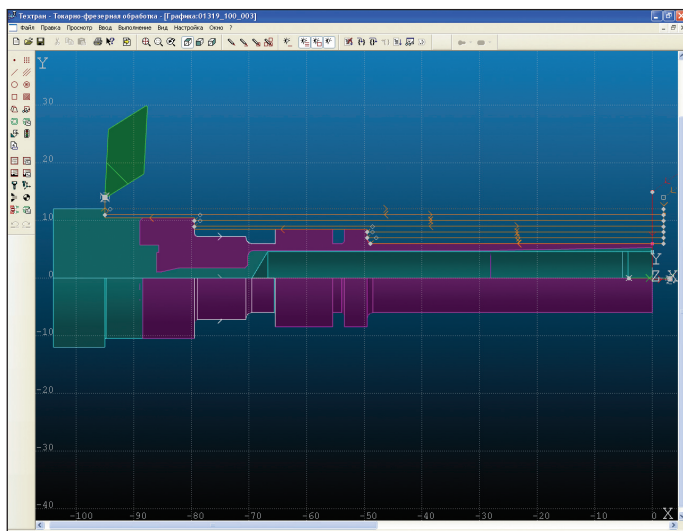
Представление токарной детали и заготовки в виде частичного разреза (вид сбоку)
